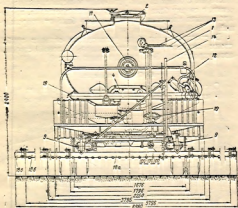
б. Общий вид автогазодренатора (вид сверху)
